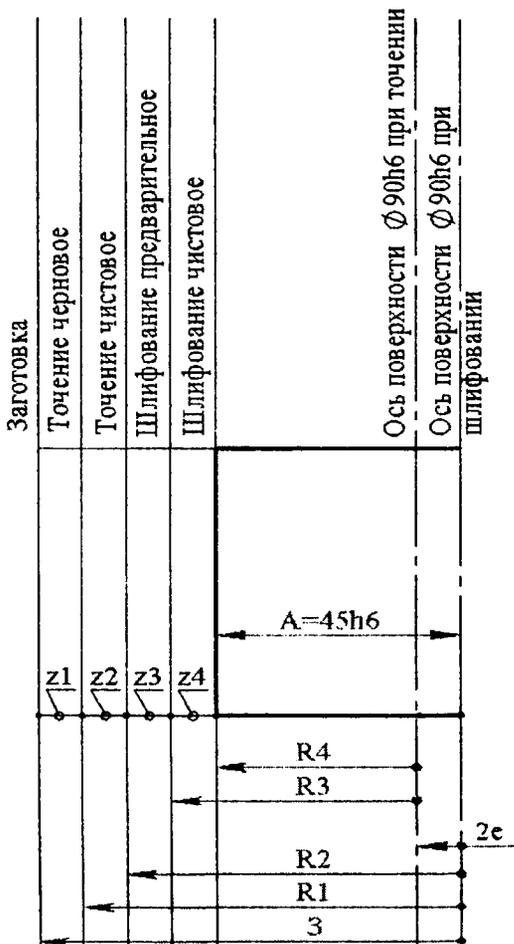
Размерная схема технологического процесса механической обработки поверхности $\varnothing 90h6$
